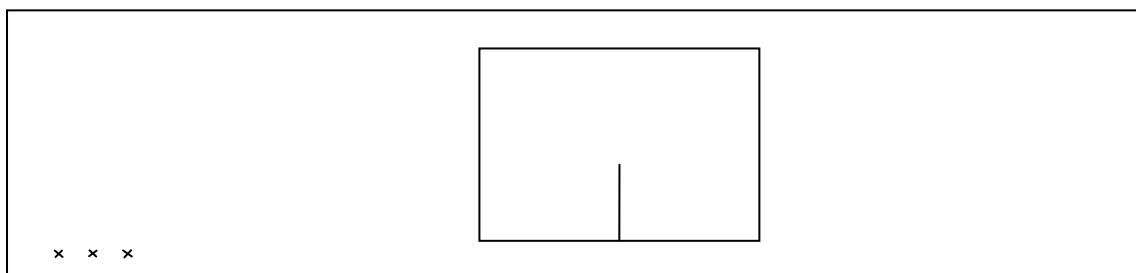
Provstavens orientering i ett provstavsämne.
